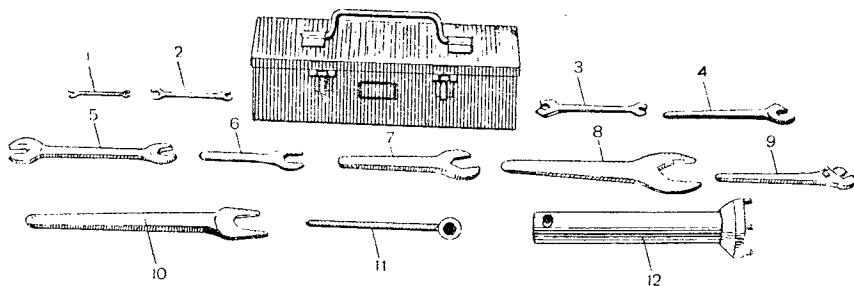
Комплектовка ящика с инструментом механика-водителя
